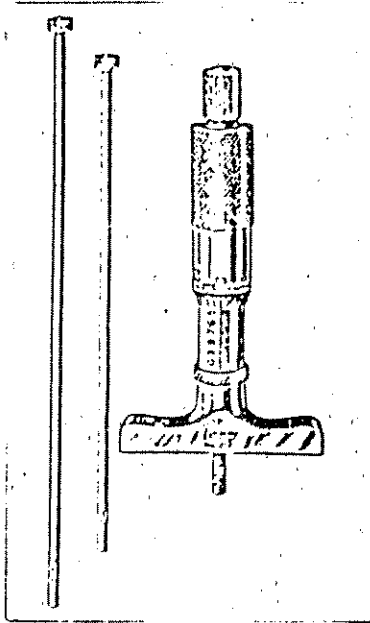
Calibrador de Profundidad con dos vástagos de extensión.
